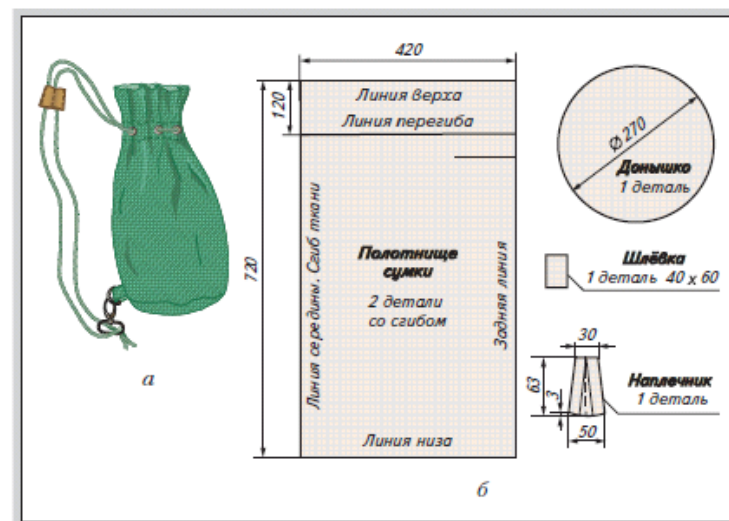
Сумка-торба: а – эскиз; б – чертёж
